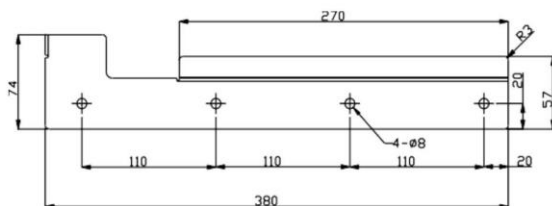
Dimensões do painel traseiro do R6-15K/17K/20K/22K/25K-T2-32
